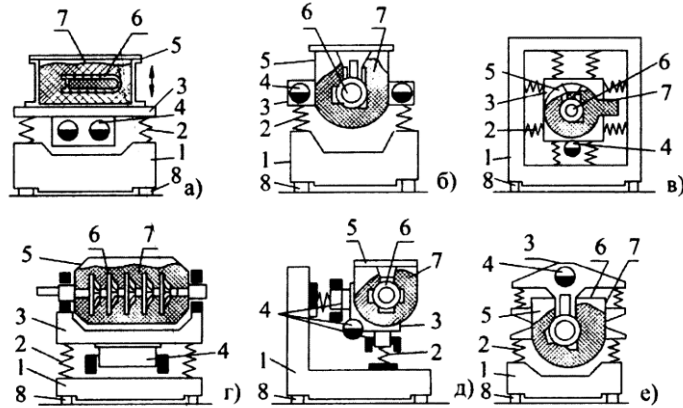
Схеми віброобробки деталей без закріплення: 1 - основа; 2 - пружні елементи; 3 - рухома рама; 4 - вібратор; 5 - контейнер; 6 - оброблювані деталі; 7 - інструментальне середовище; 8 - амортизатори
